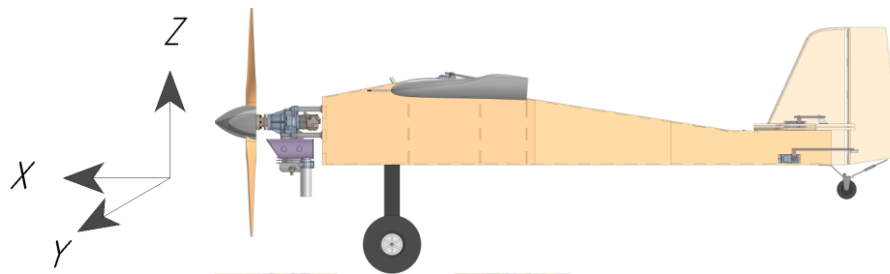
Первый вариант крепления двигателя. Без моторной рамы, цилиндром вниз
